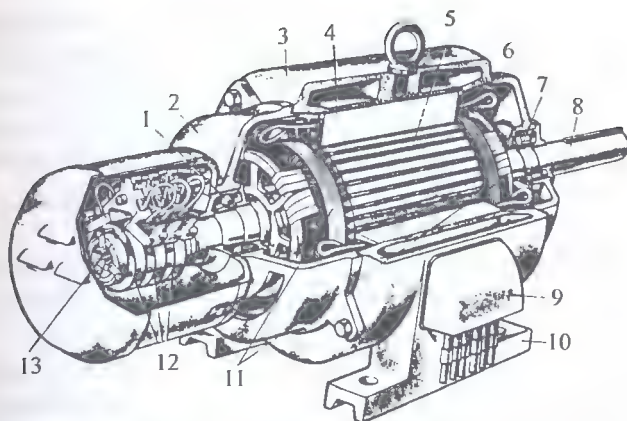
Устройство трехфазного асинхронного двигателя с фазным ротором: 1,7 — подшипники; 2,6 — подшипниковые щиты; 3 — корпус; 4 — сердечник статора с обмоткой; 5 — сердечник ротора; 8 — вал; 9 — коробка выводов; 10 — лапы; 11 — бандаж; 12 — контактные кольца; 13 — контактно-щеточный механизм
